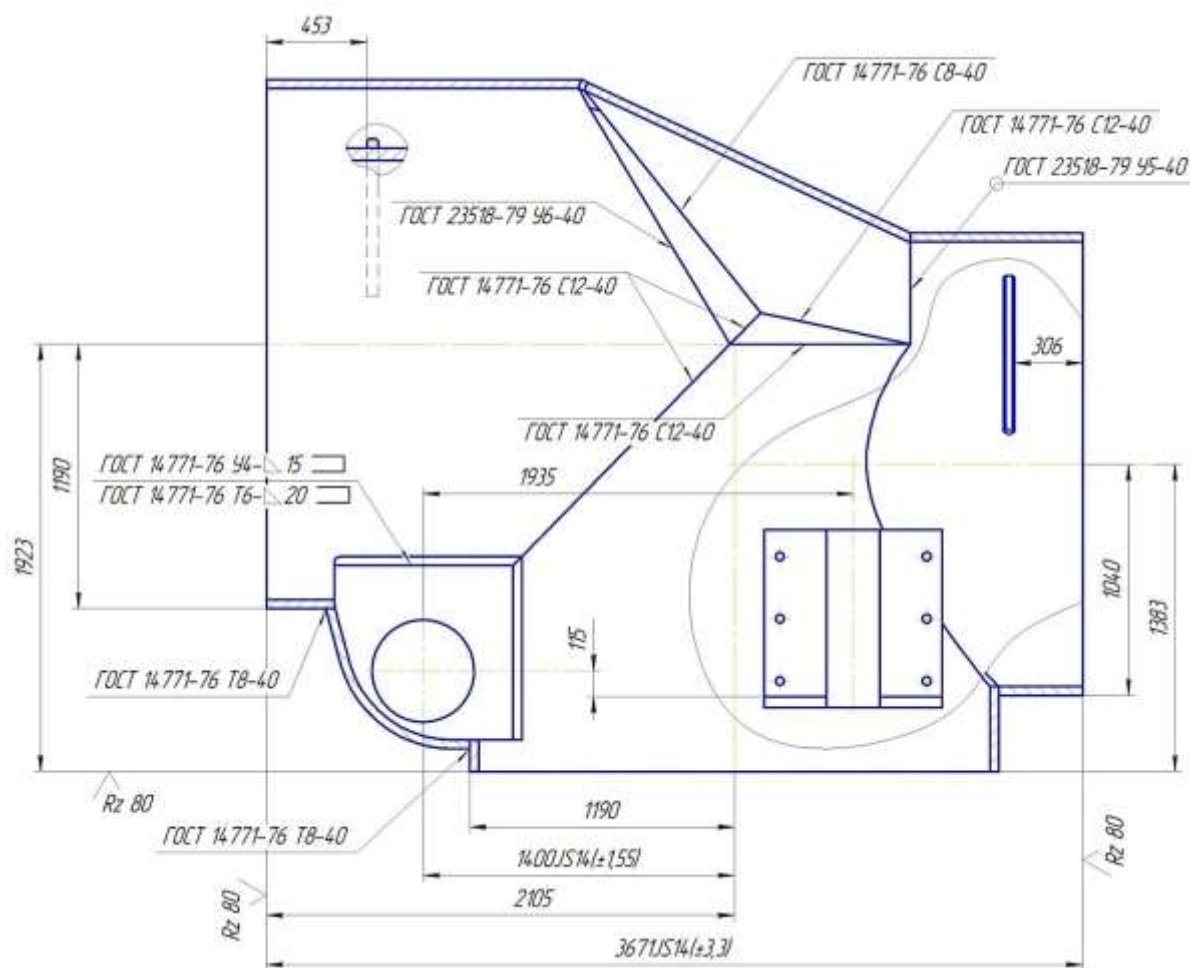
Разрез корпуса с указанием сварных швов
